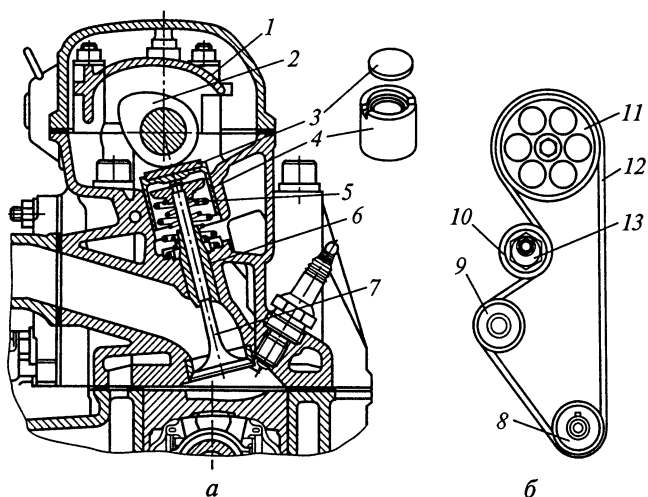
Газораспределительный механизм (а) с верхним расположением распределительного вала и его привод (б):
